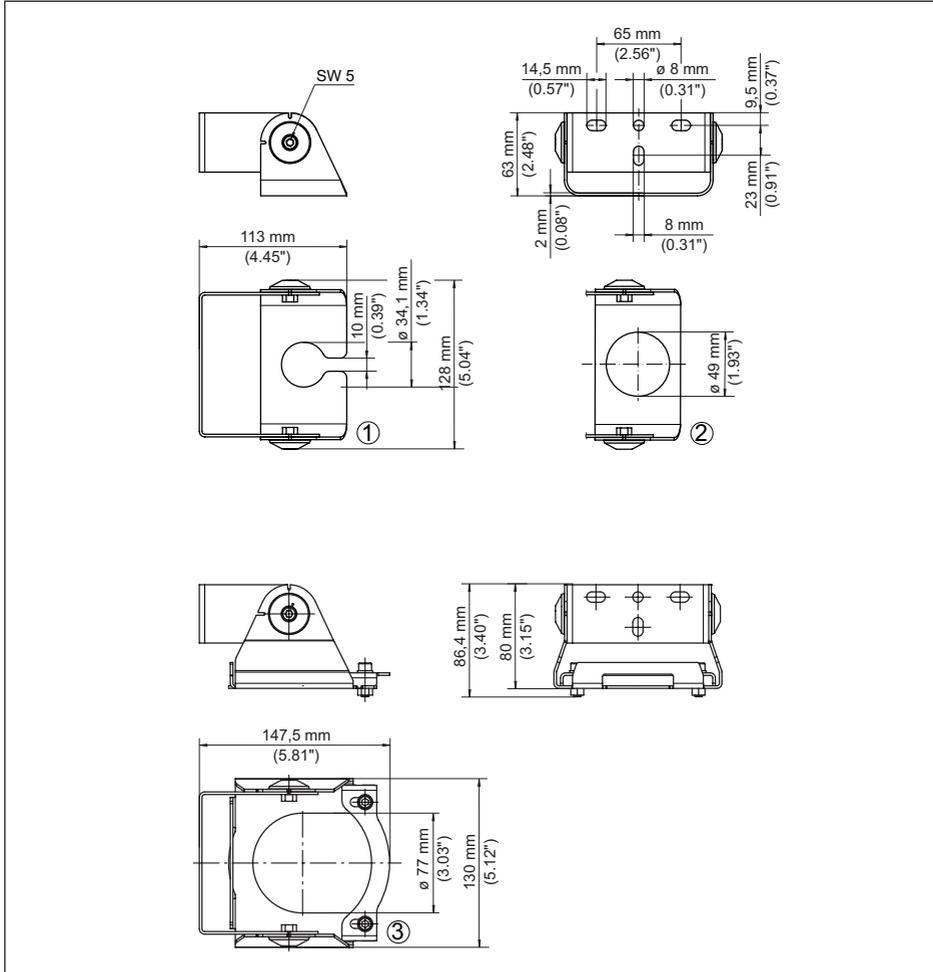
Montagebügel zur Wandmontage, Sensoraufnahme verstellbar - Ausleger 80 mm
